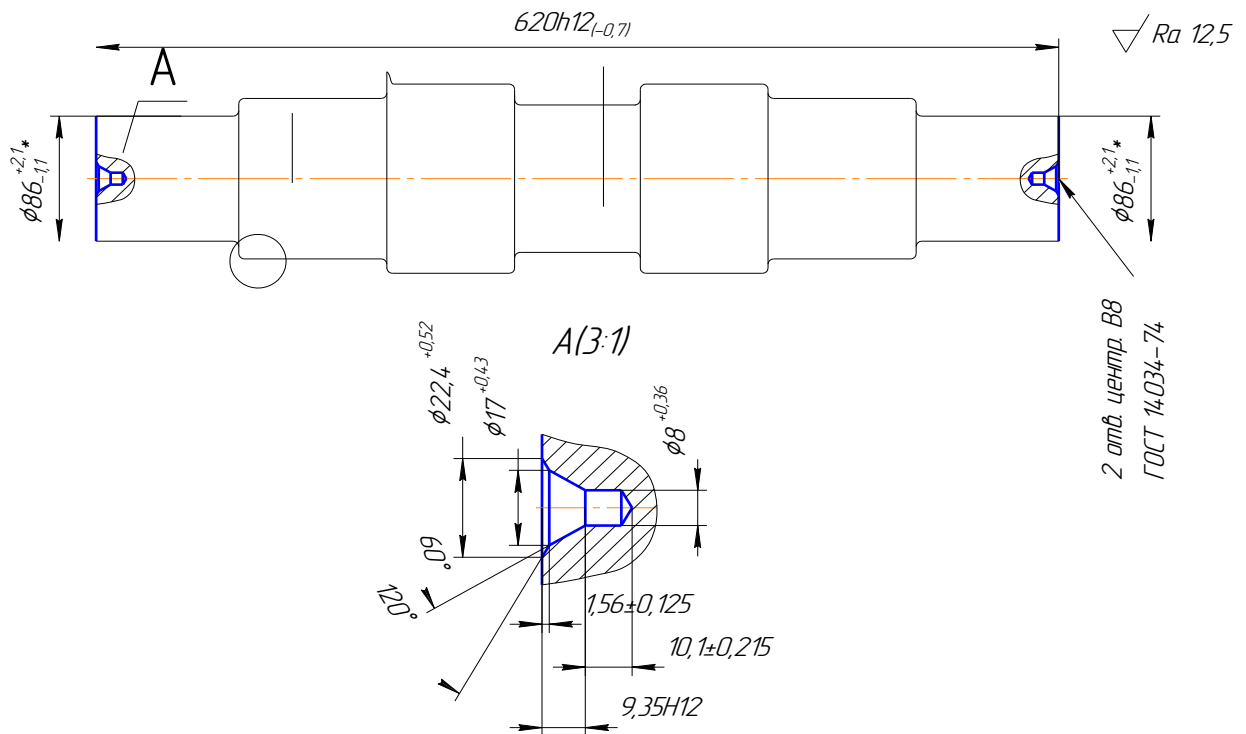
Ескіз фрезерно-центрувальної операції 030
